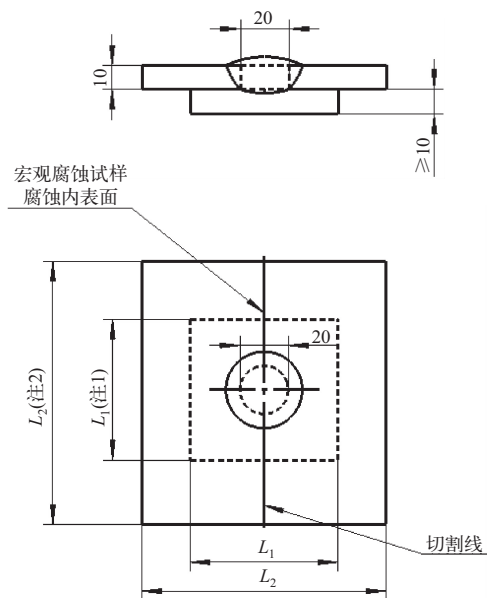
塞焊缝焊接试件形式及尺寸
